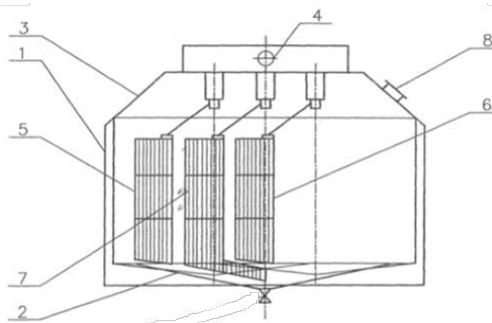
Сировиготовлювач вертикального типу [15]: 1 – резервуар; 2 – днище; 3 – кришка; 4 – привід; 5–7 – мішалки; 8 – патрубок для подачі молока
